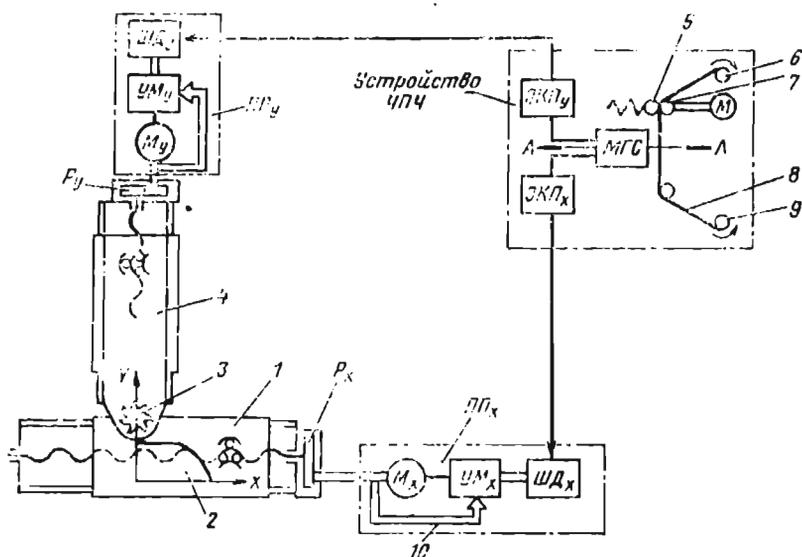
Схема импульсной системы ЧПУ фрезерного станка
